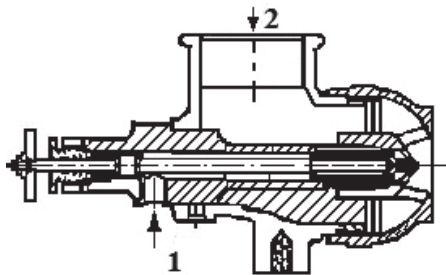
Форсунка низкого давления конструкции Карабина
